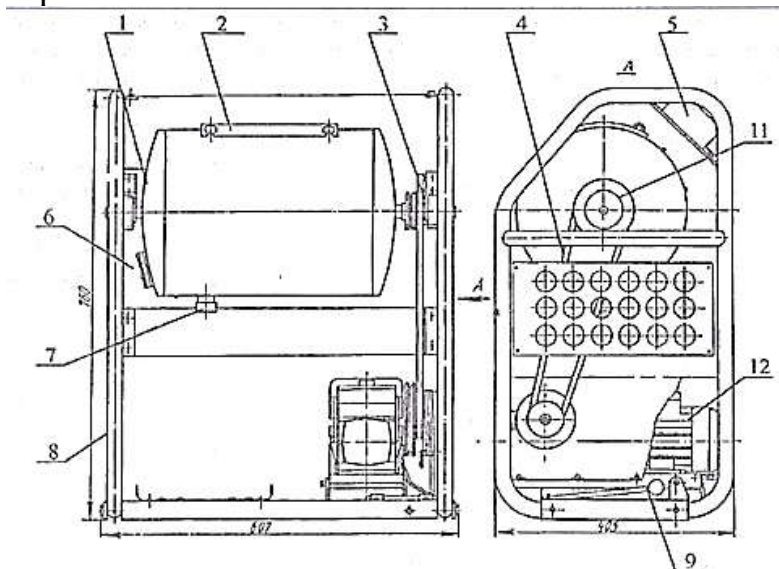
11. Загальний вид масловиготовлювача МИП-1500:
